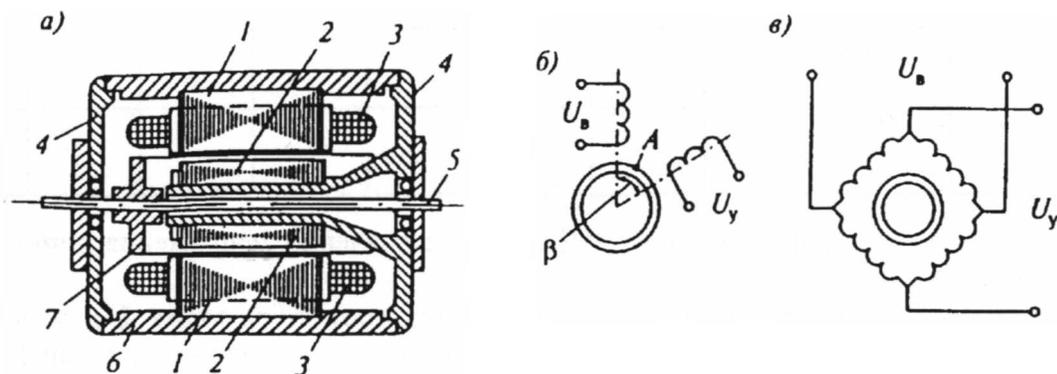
Двухфазный асинхронный исполнительный двигатель: а). конструкция; б,в). схемы соединения обмоток
